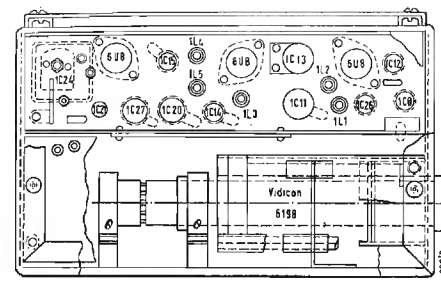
Disposizione degli elementi nella telecamera dell'impianto precedentemente citato.
